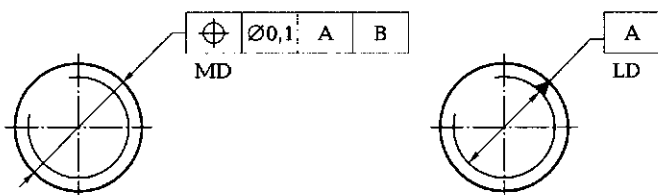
Пример обозначения геометрического допуска резьбы
